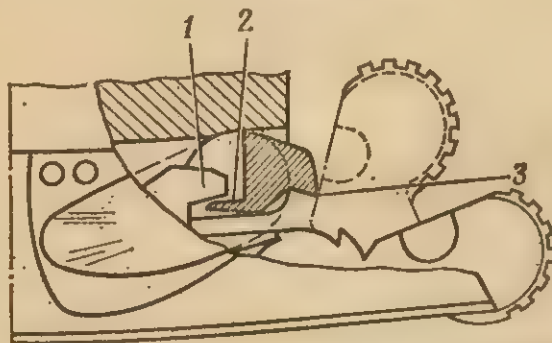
Схема блокировки курка выступом предохранителя: 1 — зуб шептала; 2 — полочка уступа предохранителя; 3 — выступ предохранителя
